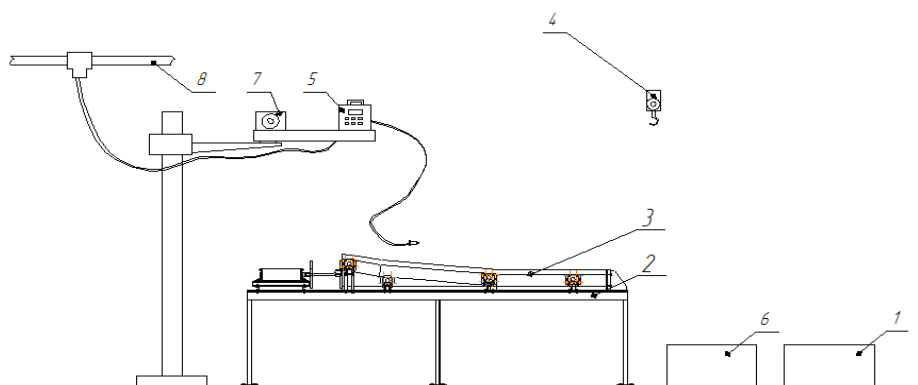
Схема компоновки рабочего места сварки подузла №3:
